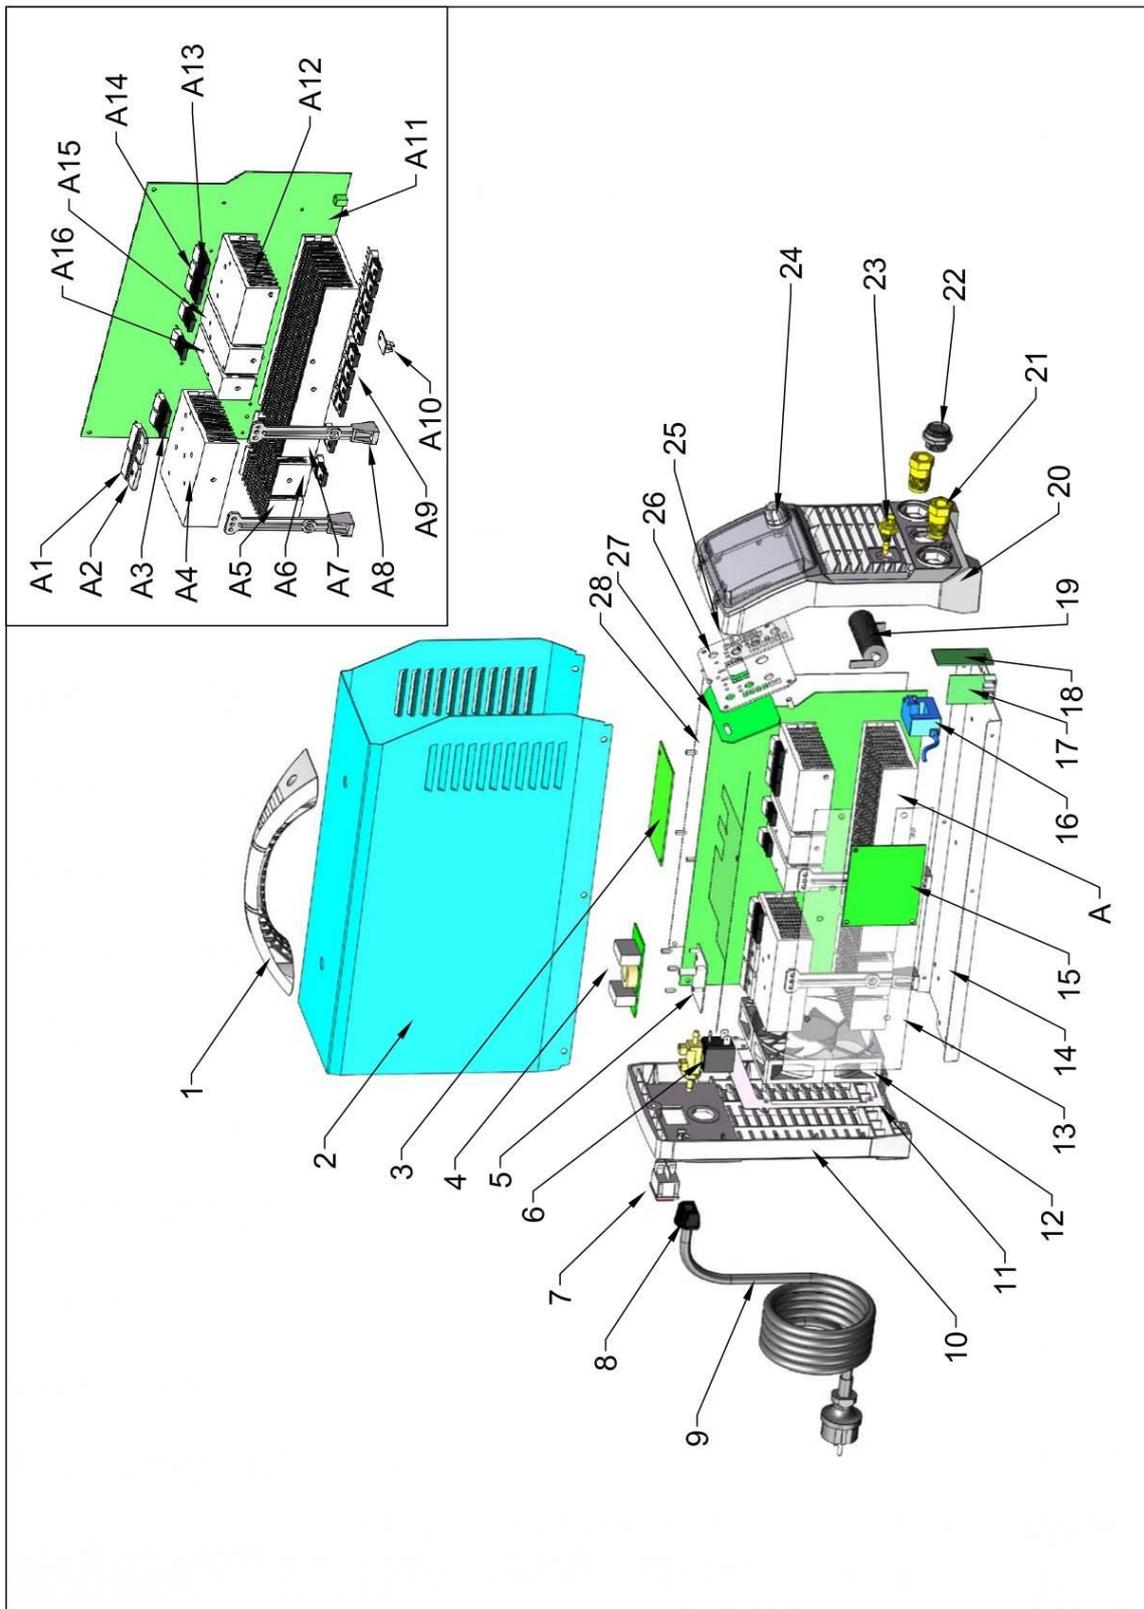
Vista explodida Joy TIG 230P AC/DC.
